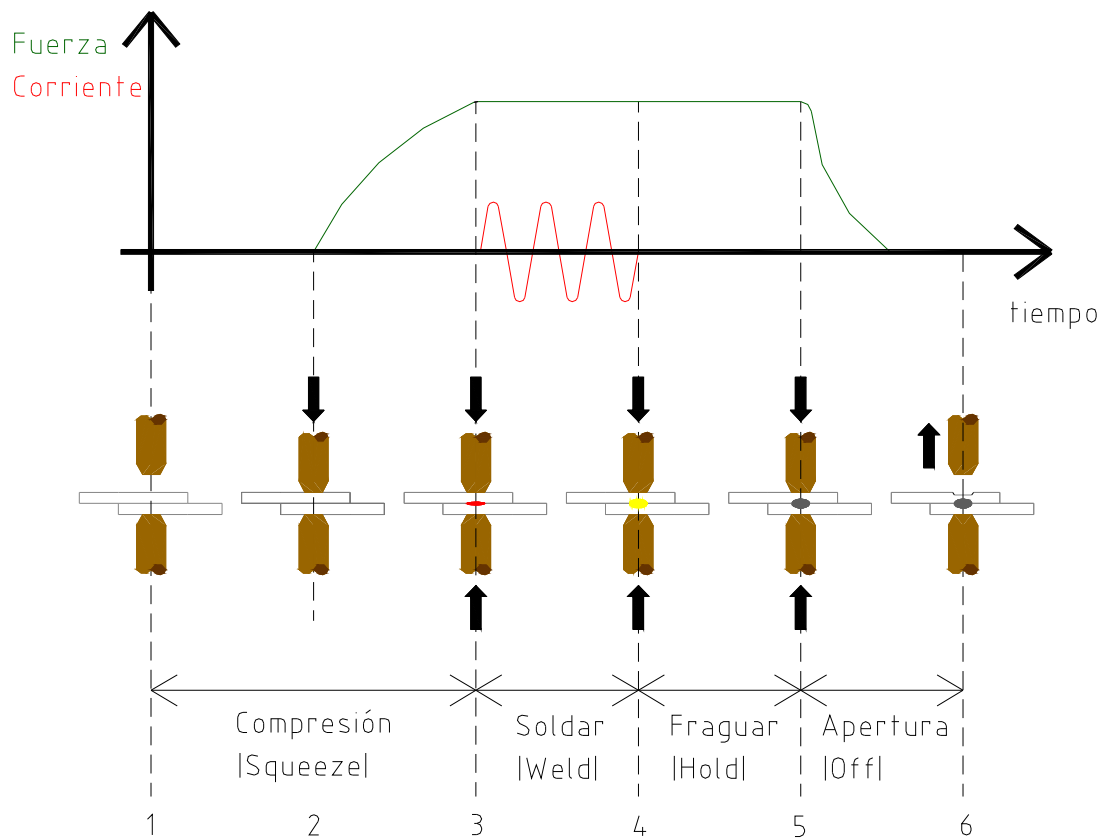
Esquema del ciclo de soldadura simple.
